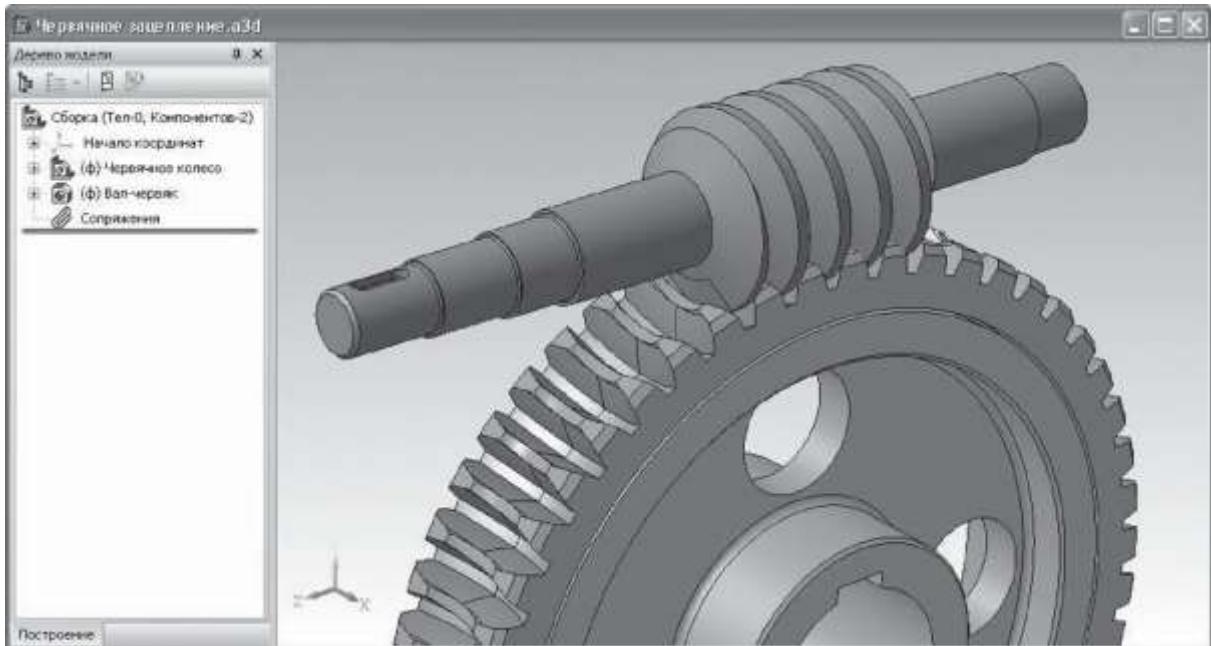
3D-модель черв'ячного зачеплення з верхнім розташуванням черв'яка
